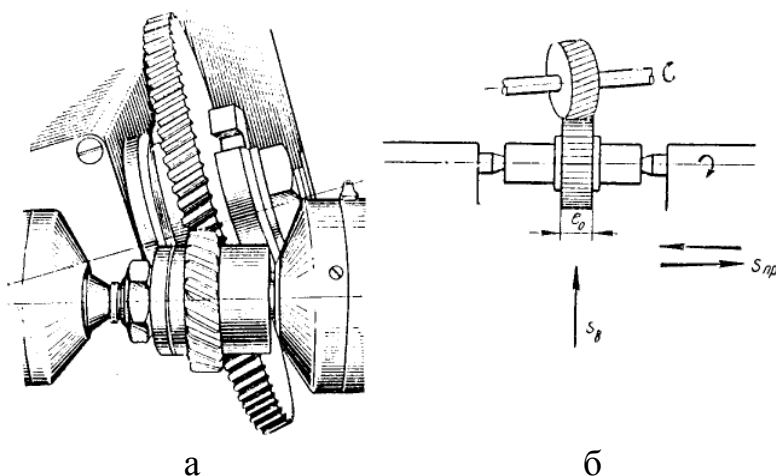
Шевінгування циліндричного зубчастого колеса дисковим шевером: а – загальний вид (подача повздовжня); б – схема шевінгування з вертикальним переміщенням столу верстата.
